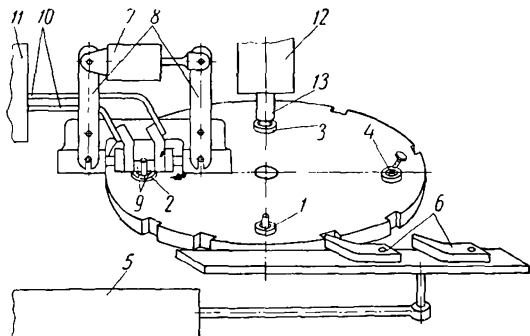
Схема устройства агрегата для электронагрева и высадки толкателя клапана
